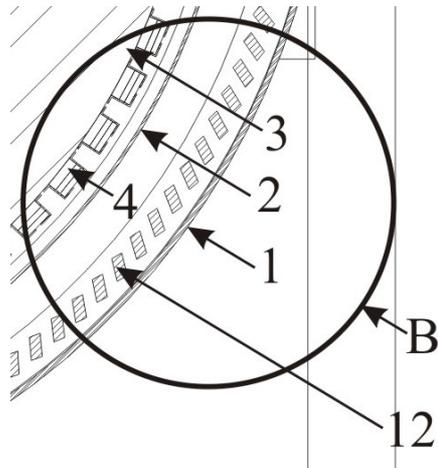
Увеличенный разрез условно принятой 3 четверти: 1 – корпус; 2 – немагнитный барабан; 3 – ярмо; 4 – магниты; 12 – индукционная решетка
